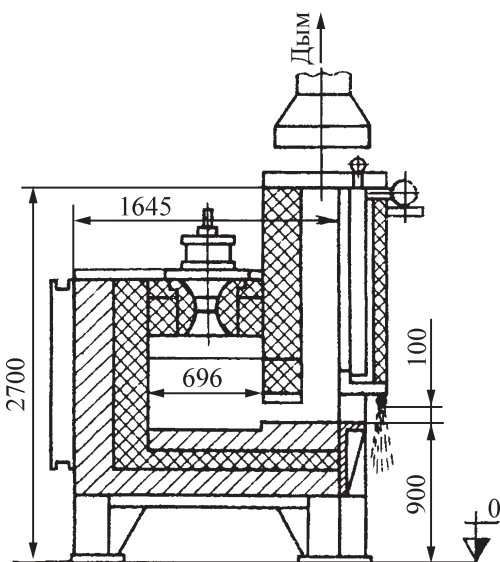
Камерная щелевая нагревательная печь с обогревом плоскопламенной горелкой
